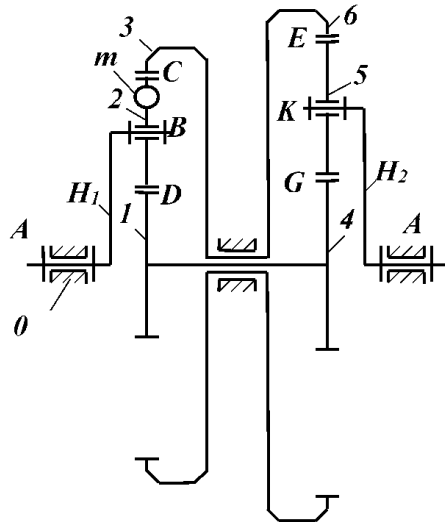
Зубчатый адаптивный вибрационный механизм
